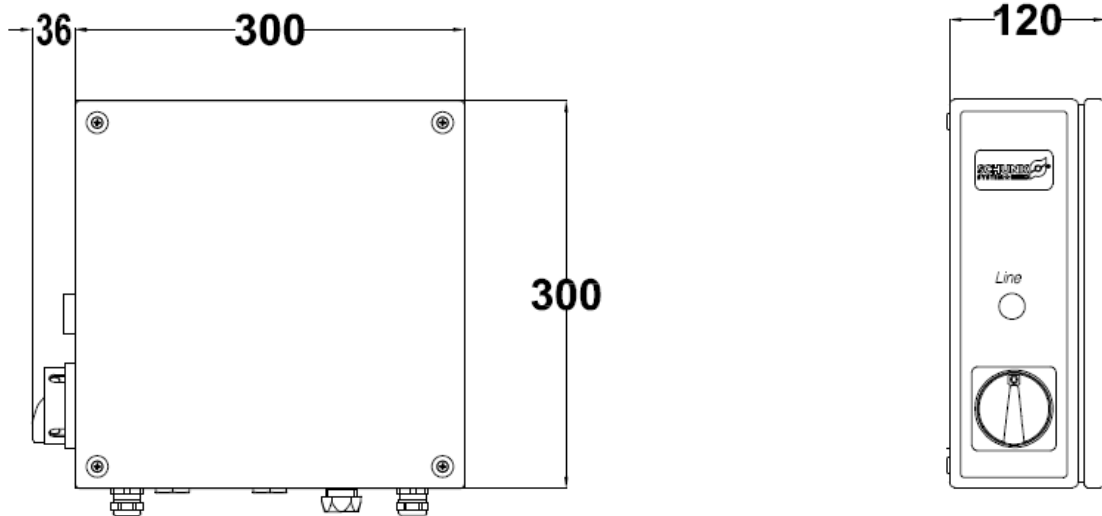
Dimensioni REBOX.1-SC, REBOX.1D-SC und REBOX.2-SC
